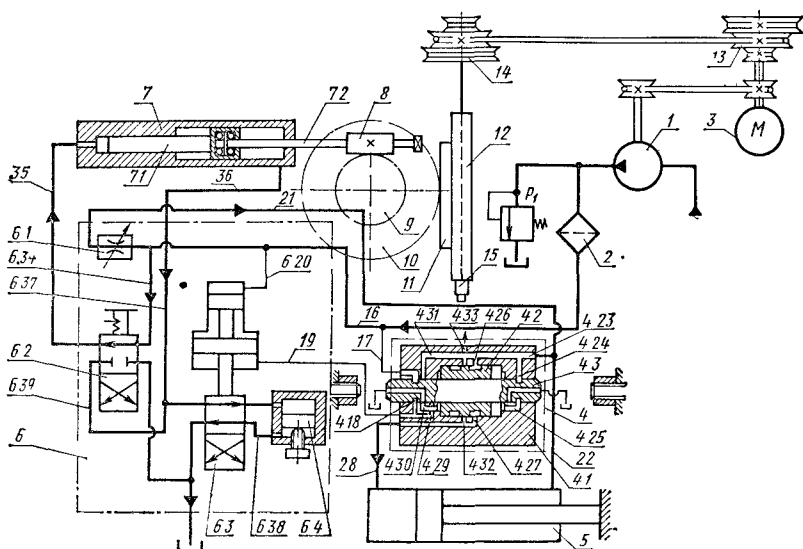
Гидрокинематическая схема шпоночно-фрезерного станка
